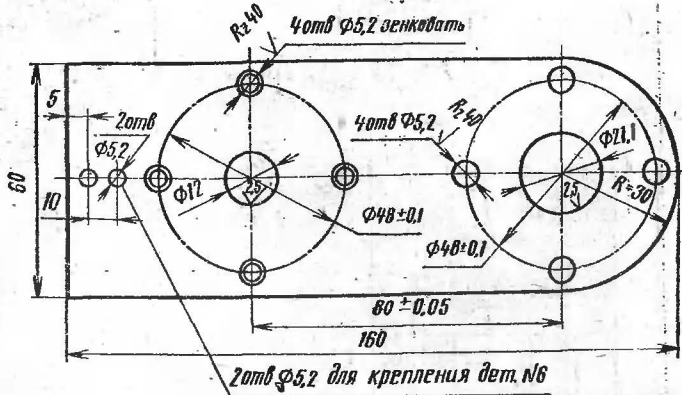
Конструкция пластины крепления шпиндельной втулки
